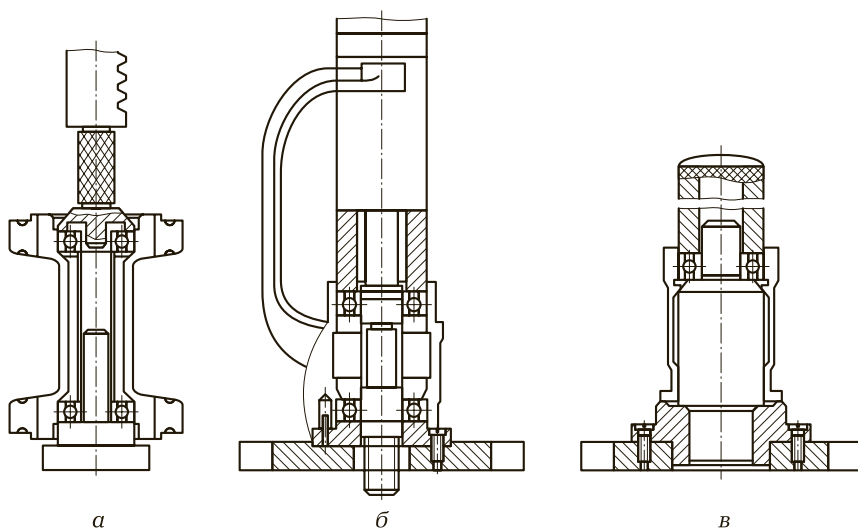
Приспособления для обеспечения ориентации подшипника относительно оси отверстия при его запрессовывании в корпус:
